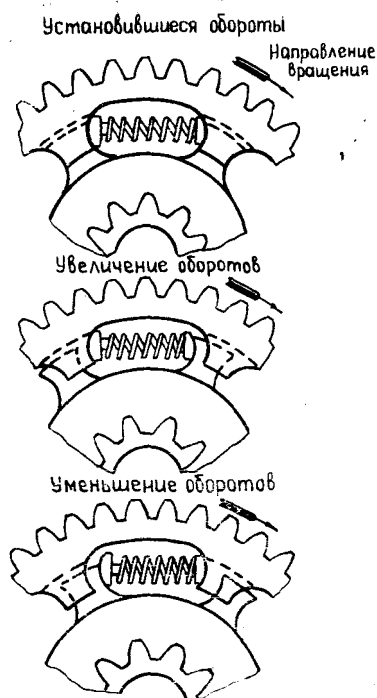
Схема работы двойной эластичной шестерни привода механизма газораспределения
